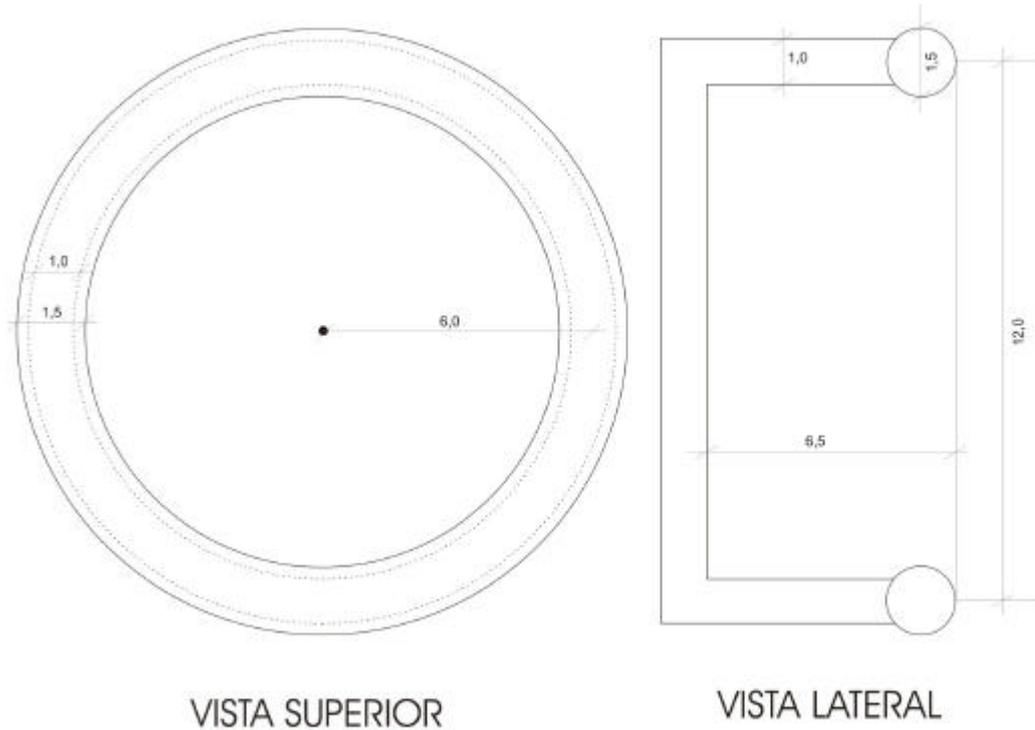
Desenho técnico dos ninhos , dimensões em cm
